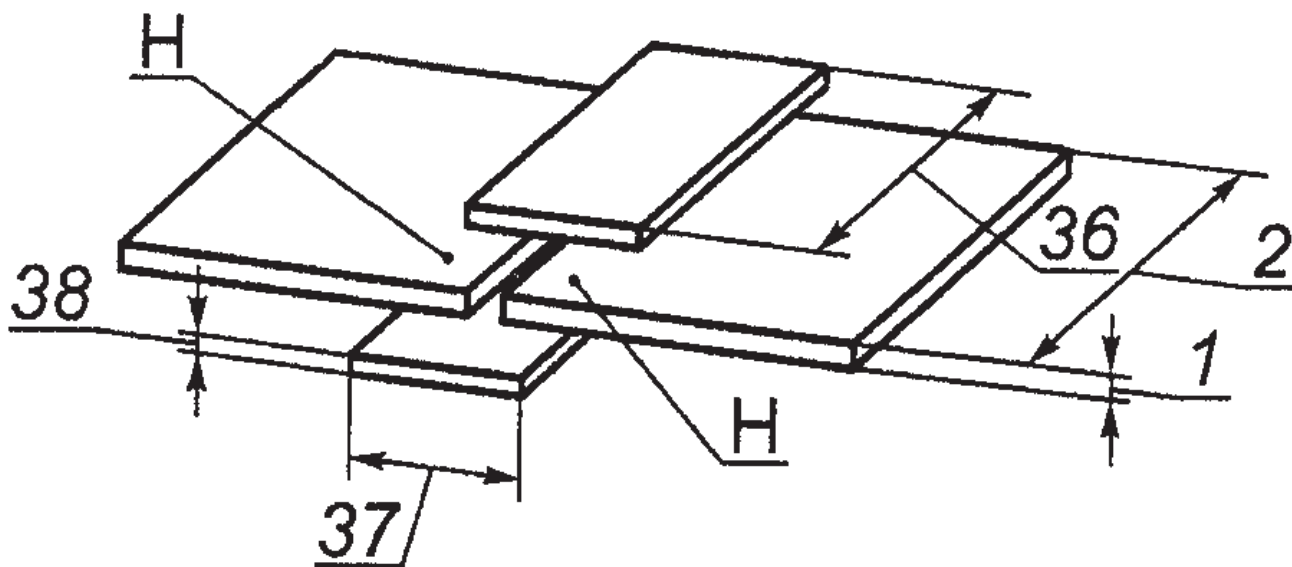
Сборка под шовную контактную стыковую сварку по фольге Figure 11. Configuration for foil-seam-welds Figure 11. Configuration pour soudure
